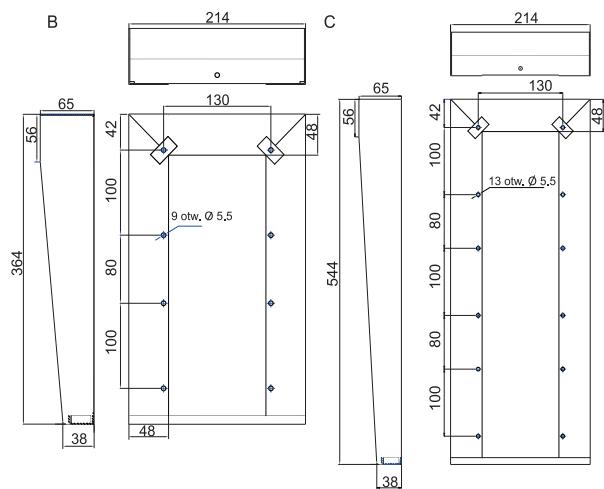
Габаритные размеры накладных корпусов для блока вызова СР-2501xx в вертикальном положении
